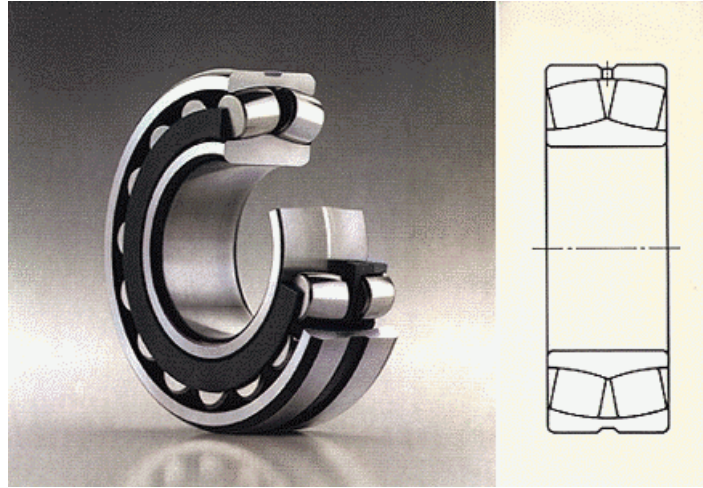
Rodamiento oscilante de rodillos (o de rodillos esféricos) de doble hilera.
